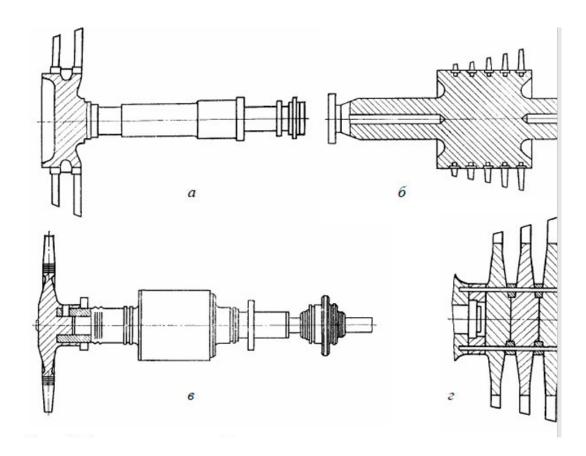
Роторы газовых турбин: a — ротор с консольным диском, откованным заодно с валом; δ — цельнокованный барабанный ротор; ϵ — консольный ротор с закрепленным на валу диском; ϵ — сборный ротор с дисками, соединенными стяжным болтом
